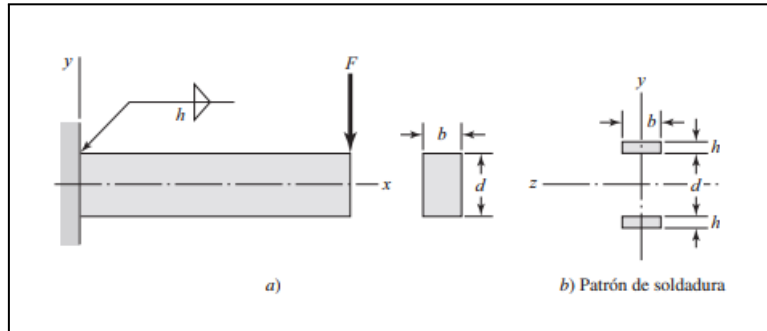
Soldadura en ambas caras de un voladizo
